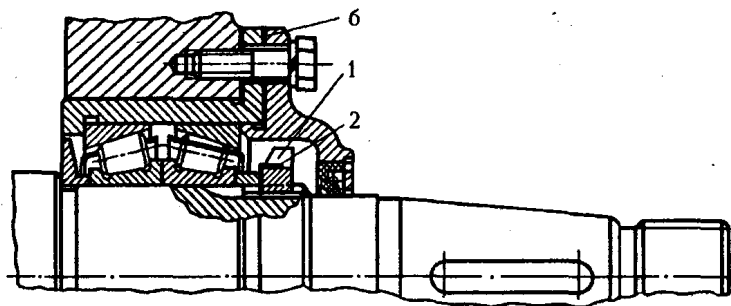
Конструктивні особливості опор валів із двома кульковими і роликовими радіально-упорними підшипниками
